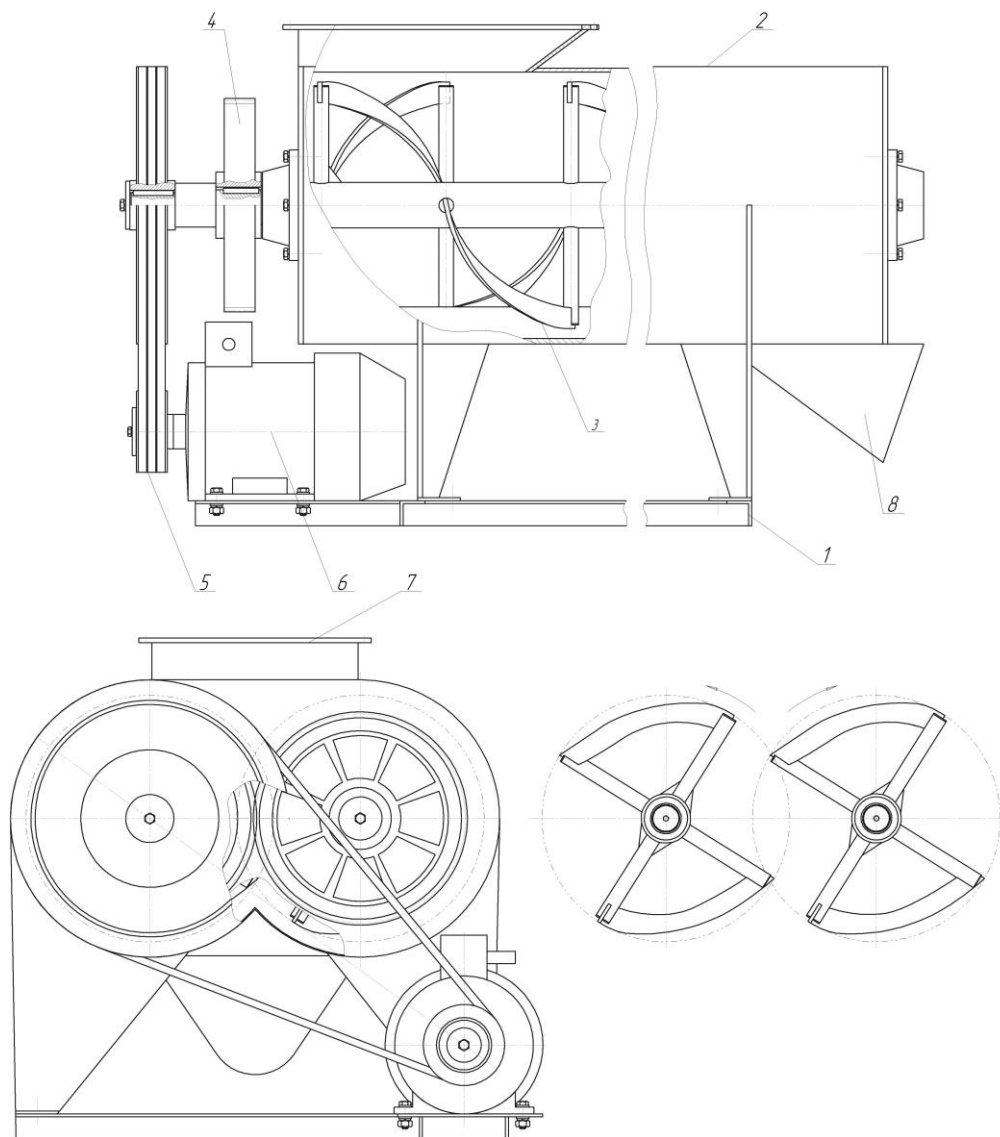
Розроблений змішувач компонентів: 1 – станина; 2 – корпус; 3 – робочий орган; 4 – зубчаста передача; 5 – пасова передача; 6 – електродвигун; 7 – завантажувальна горловина; 8 – вивантажувальна горловина.
